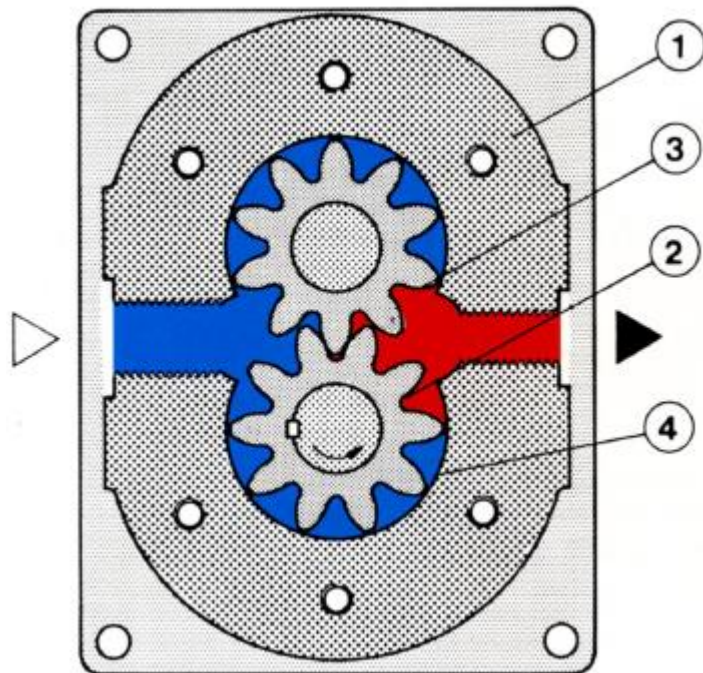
Bomba de engranaxes con dentado exterior [3]
